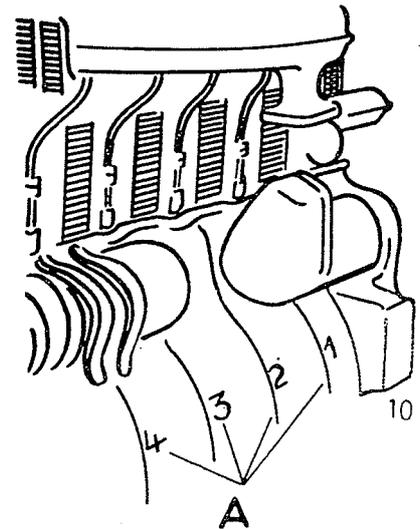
Zylinderbezeichnung im Motorgehäuse eingegossen
